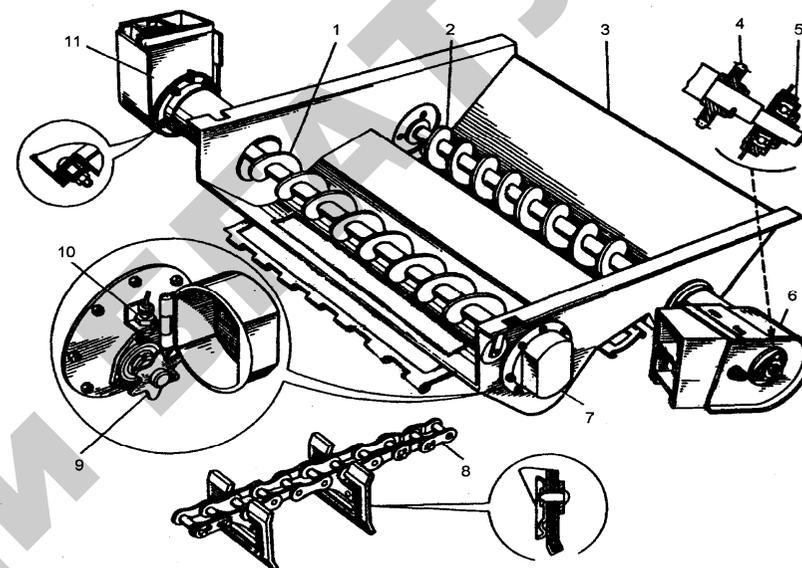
Блок шнеков: 1 — шнек зерновой; 2 — шнек колосовой; 3 — корпус; 4, 9 — звездочка; 5 — подшипник; 6 — элеватор колосовой; 7 — крышка; 8 — цепь; 10 — датчик; 11 — элеватор зерновой
